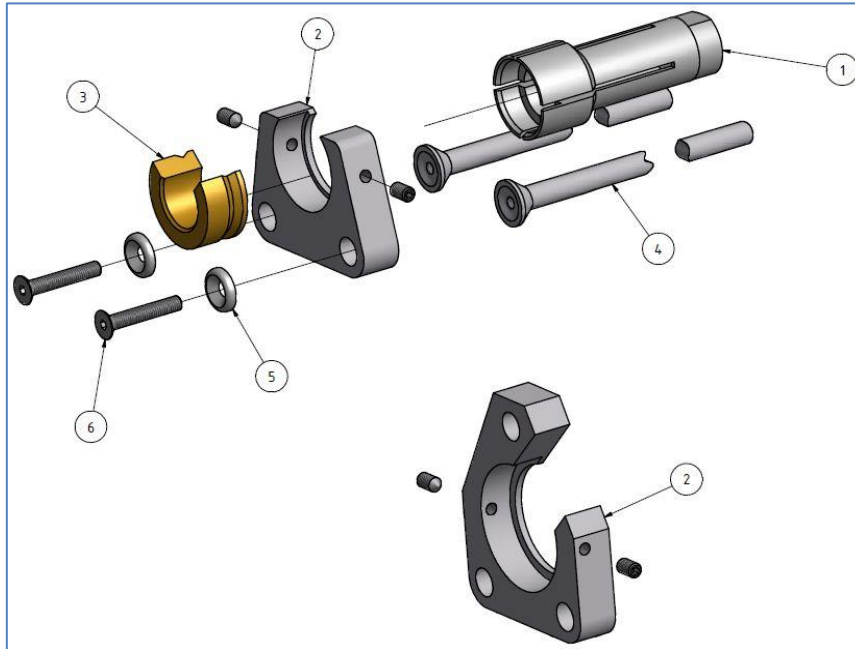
Stützeinrichtung für Kopfbolzen ab 50 mm Länge
